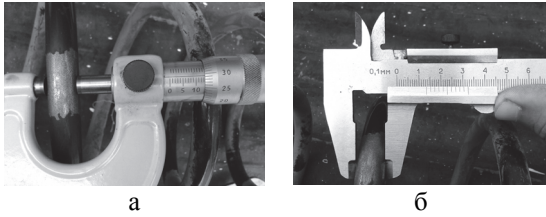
Измерение  $d$  проволоки витков пружин: а – микрометром; б –мштангенциркулем
